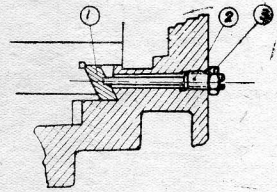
Регулировка натяжения пружины подающего червяка фартука
